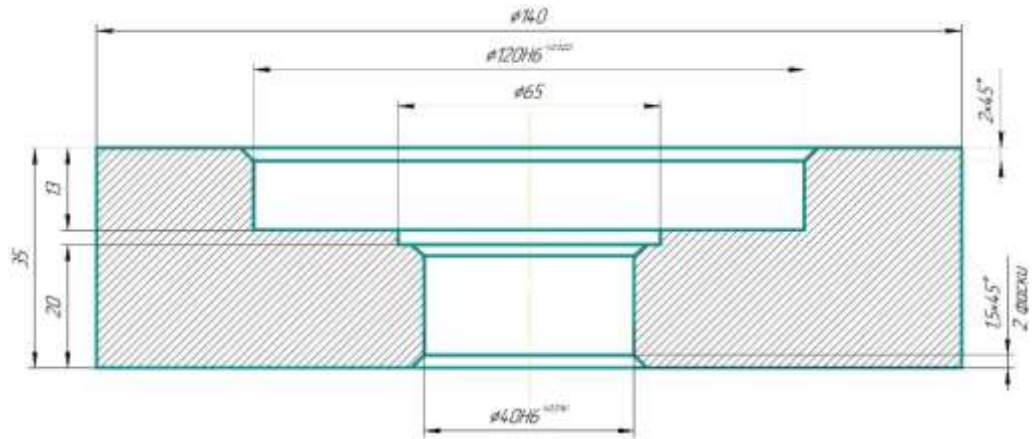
Центрирующее приспособление для сборки деталей клевого соединения «промежуточный вал-подшипник» коробки передач КАМАЗ-4310
